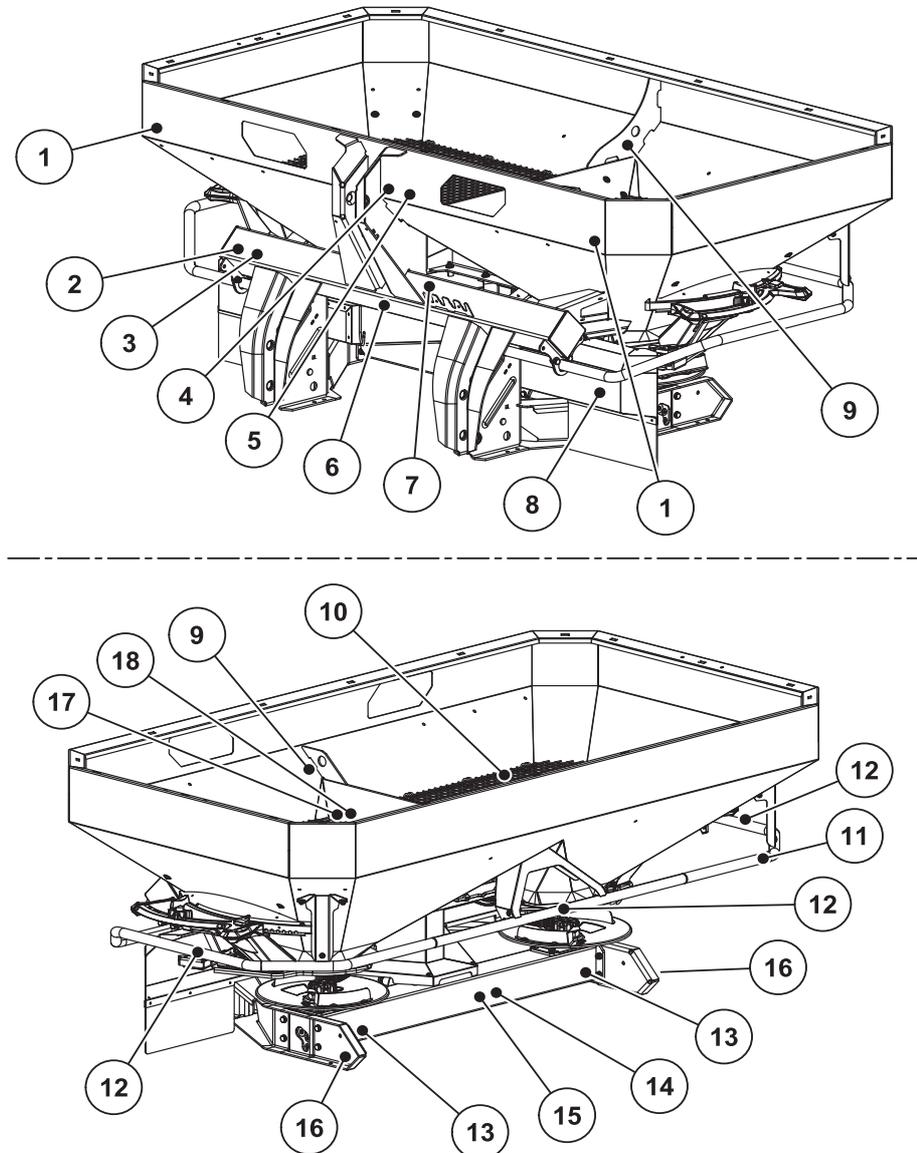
Position des dispositifs de protection, des étiquettes d'avertissement et d'instruction et des réflecteurs
